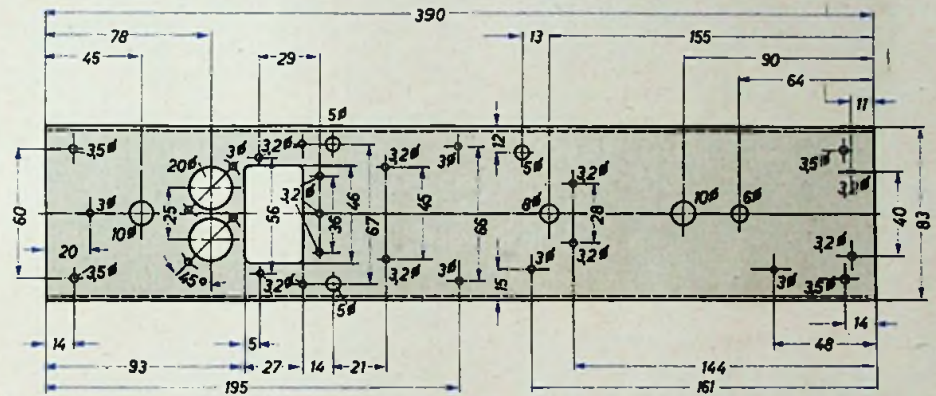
Abmessungen und Bohrungen des Chassis der Send-Endstufe
